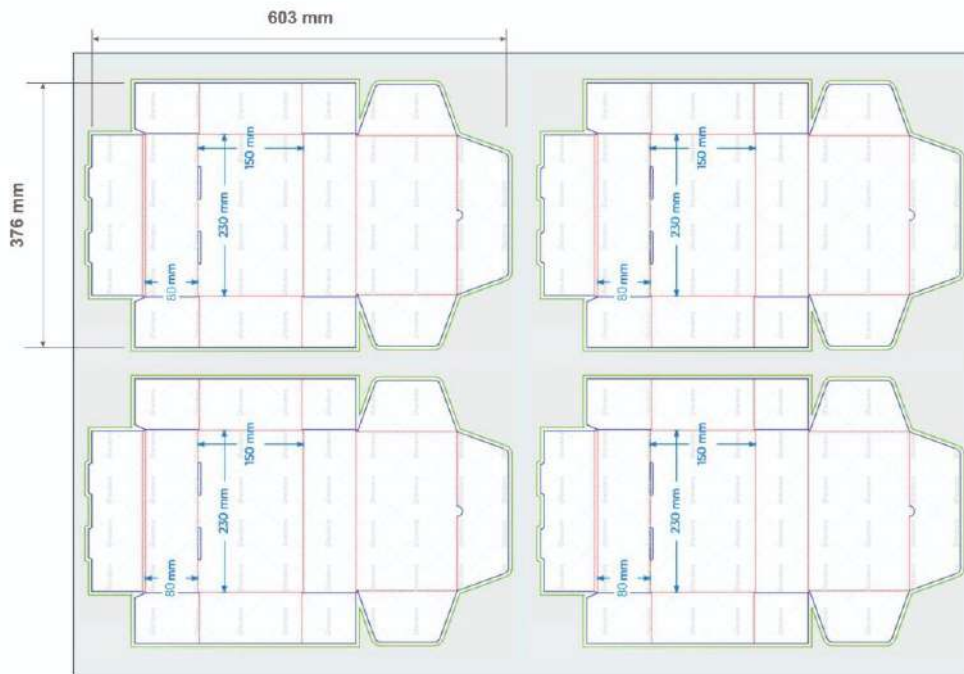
Disposición de cajas para hamburguesa por plancha.
